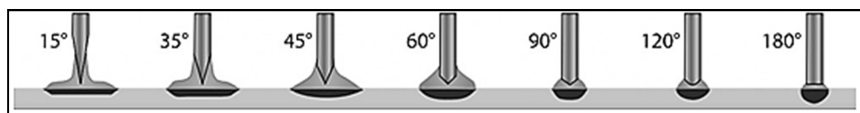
Efeito da variação do ângulo da ponta do eletrodo de tungstênio sobre o perfil do geométrico do cordão de solda (Adaptado de R-Techwelding Co).
